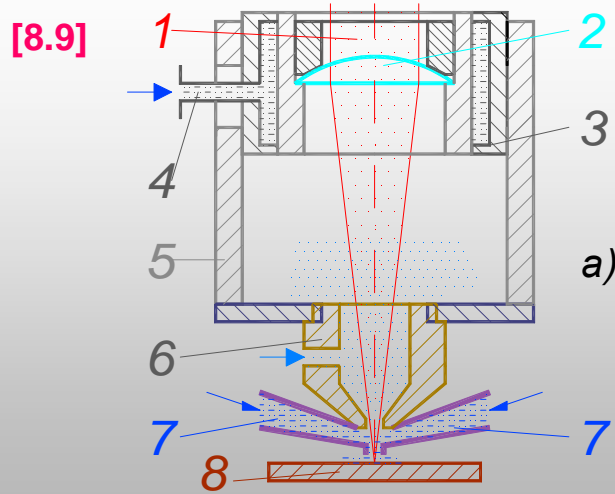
(12.8,9). Різки для обробки заготовок з одночасним їх змочуванням
